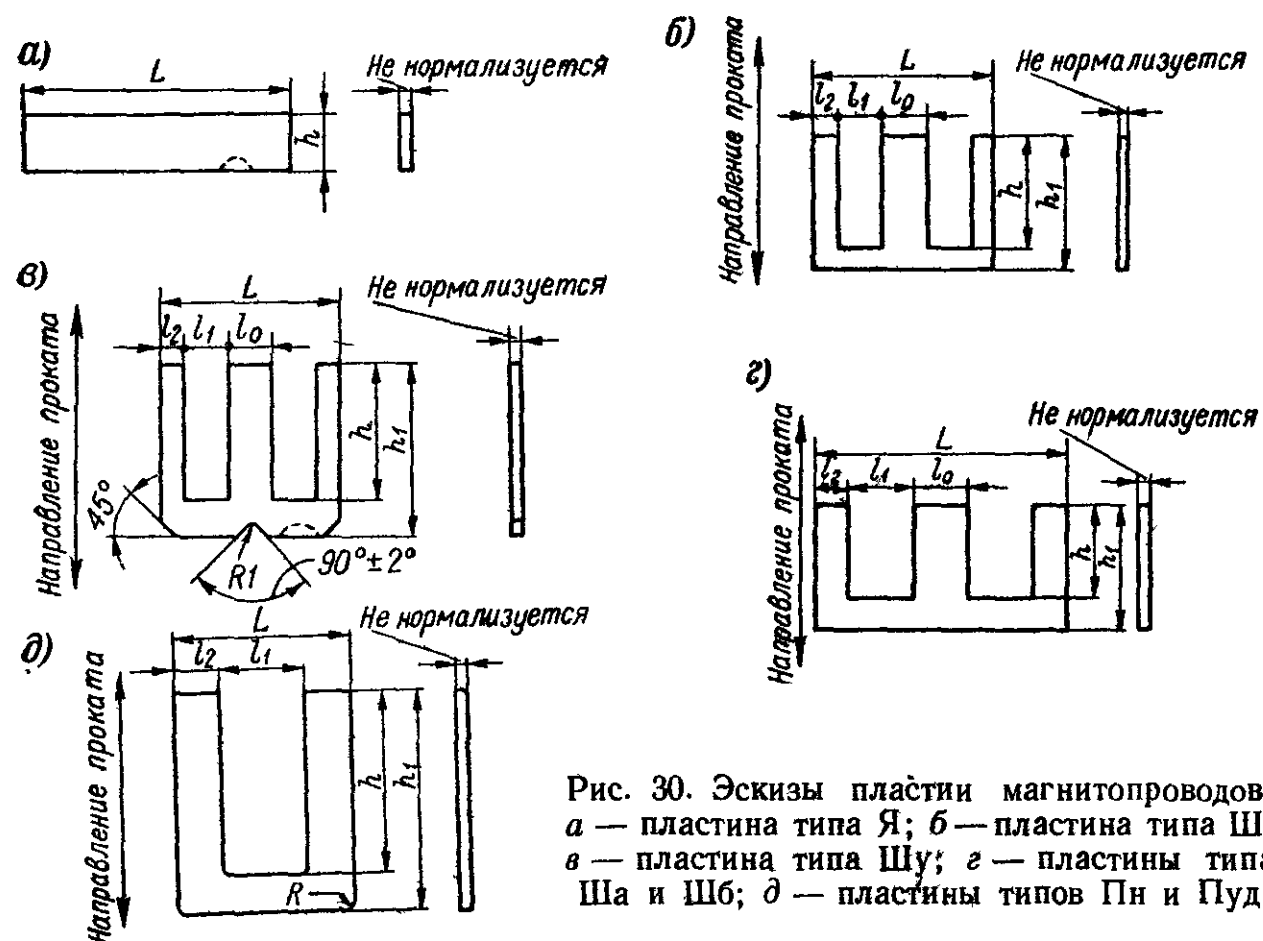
Эскизы пластины магнитопроводов: а — пластина типа Я; б — пластина типа Ш; в — пластина типа Шу; г — пластины типа Ша и Шб; д — пластины типов Пн и Пуд
